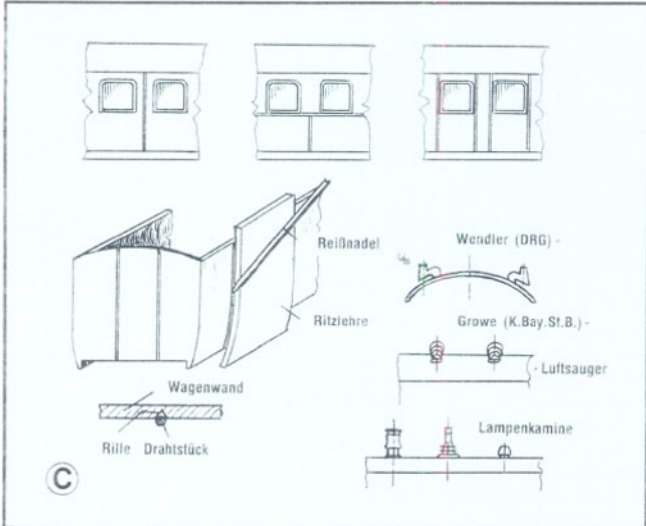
Zur Anordnung der Deckleisten an den Wagenwänden und zu den Dachaufbauten.
